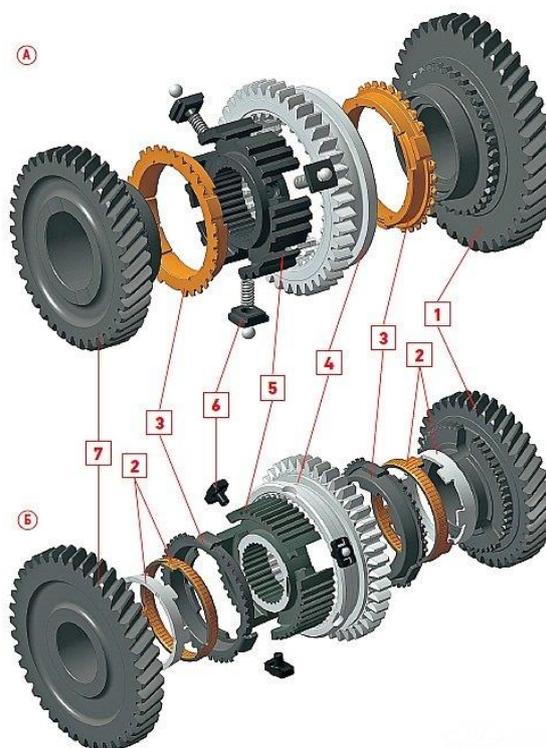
Устройство синхронизаторов коробки передач LADA GRANTA
